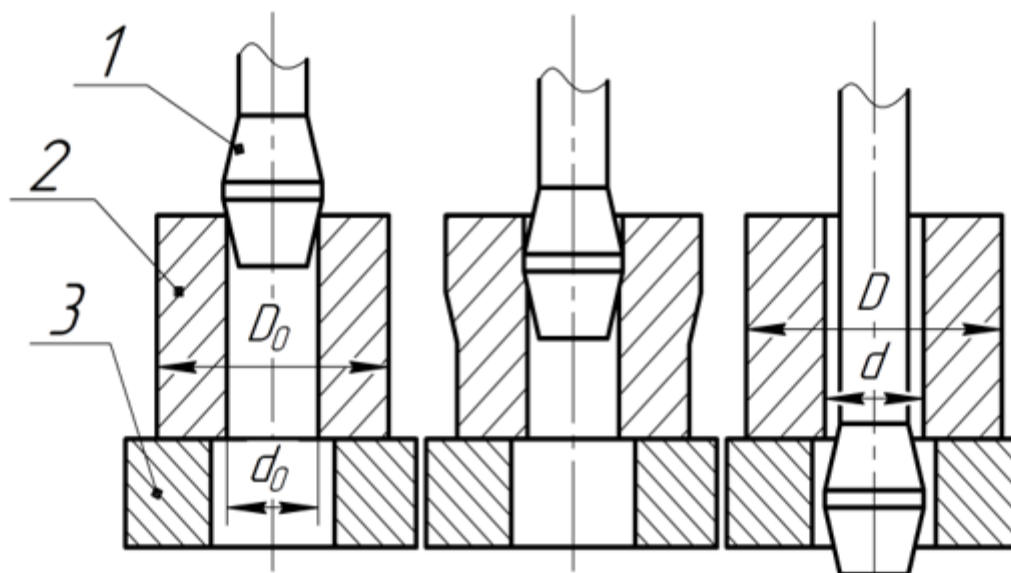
Принципиальная схема процесса дорнования(1)дорн; (2)образец; (3)опор; (d_0)внутренний диаметр заготовки; (D_0) - внешний диаметр заготовки; (d)заготовка внутреннего диаметра после сгорания; (D)заготовка после сгорания Наружный диаметр
